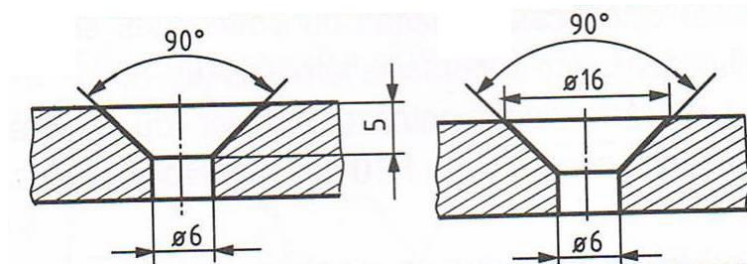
Representação em desenho técnico para cotagem de escareados.
